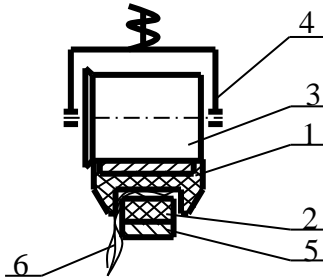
Поперечний розріз робочої ділянки затискного транспортера тіпальної машини агрегату МТ-100-Л: 1 – ведучий пас; 2 – ведений пас; 3 – притискний ролик; 4 – притискний пристрій; 5 – опора; 6 – оброблювальний матеріал
